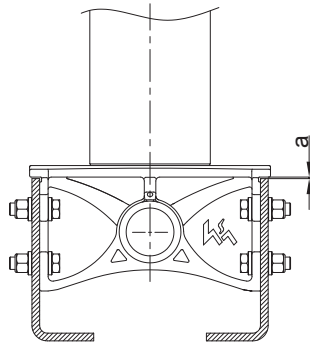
H Tipi Braket Bağlantısı - Boşluk Gösterimi
